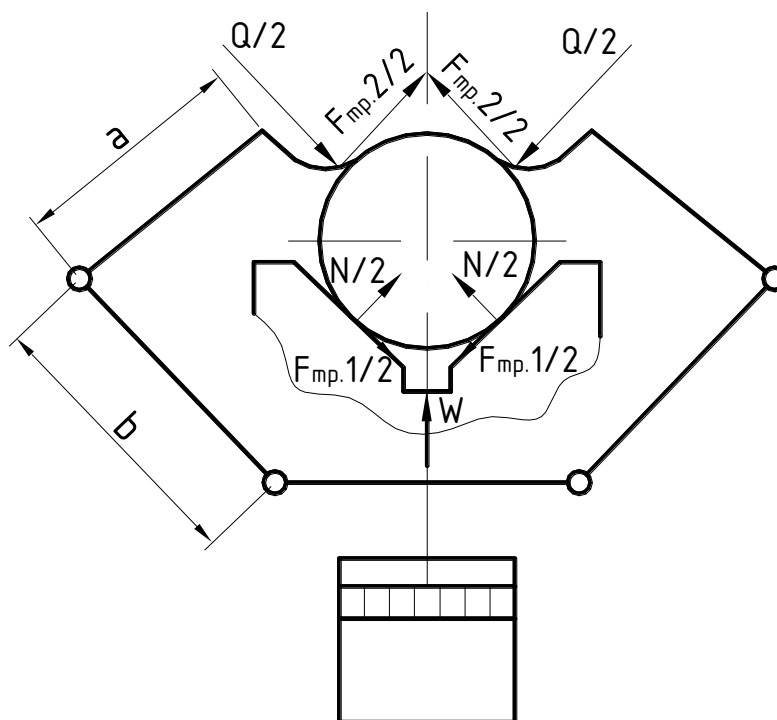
Розрахункова схема для визначення необхідної сили затиску
